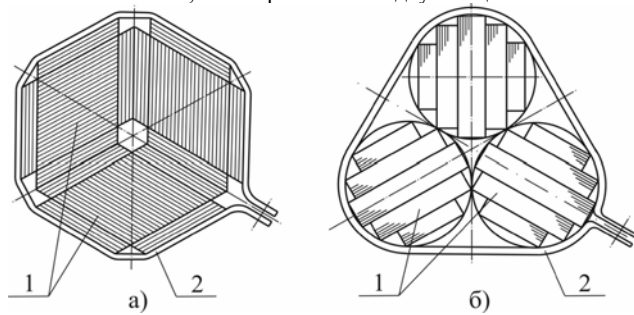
Сборка для обработки торцевых поверхностей стержней пространственных магнитных систем с параллельными (а) и цилиндрическими (б) образующими поверхностями: 1 – стержень; 2 – крепежное приспособление (хомут)
